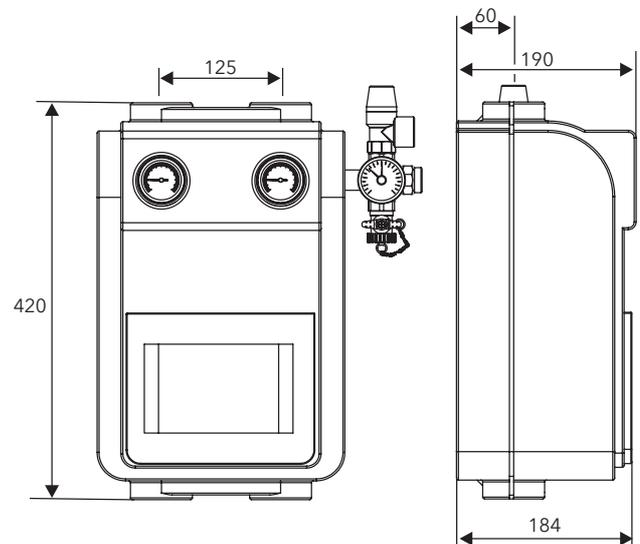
CIRCO 5 in Vorder- und Seitenansicht mit Bemaßung in mm
